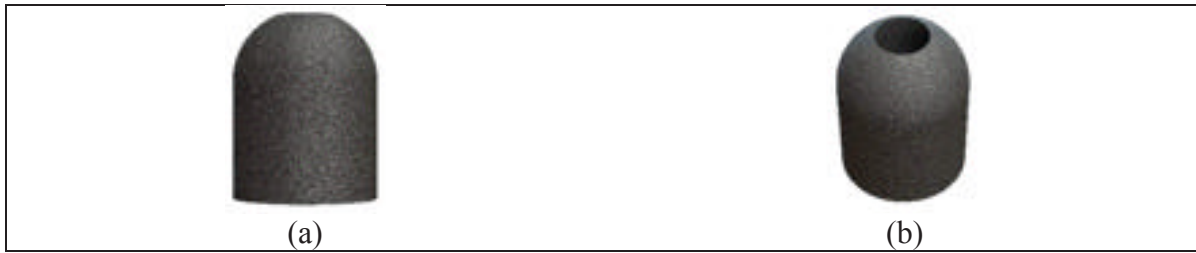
Meule de type embout (a) Vue de face (b) Vue isométrique
